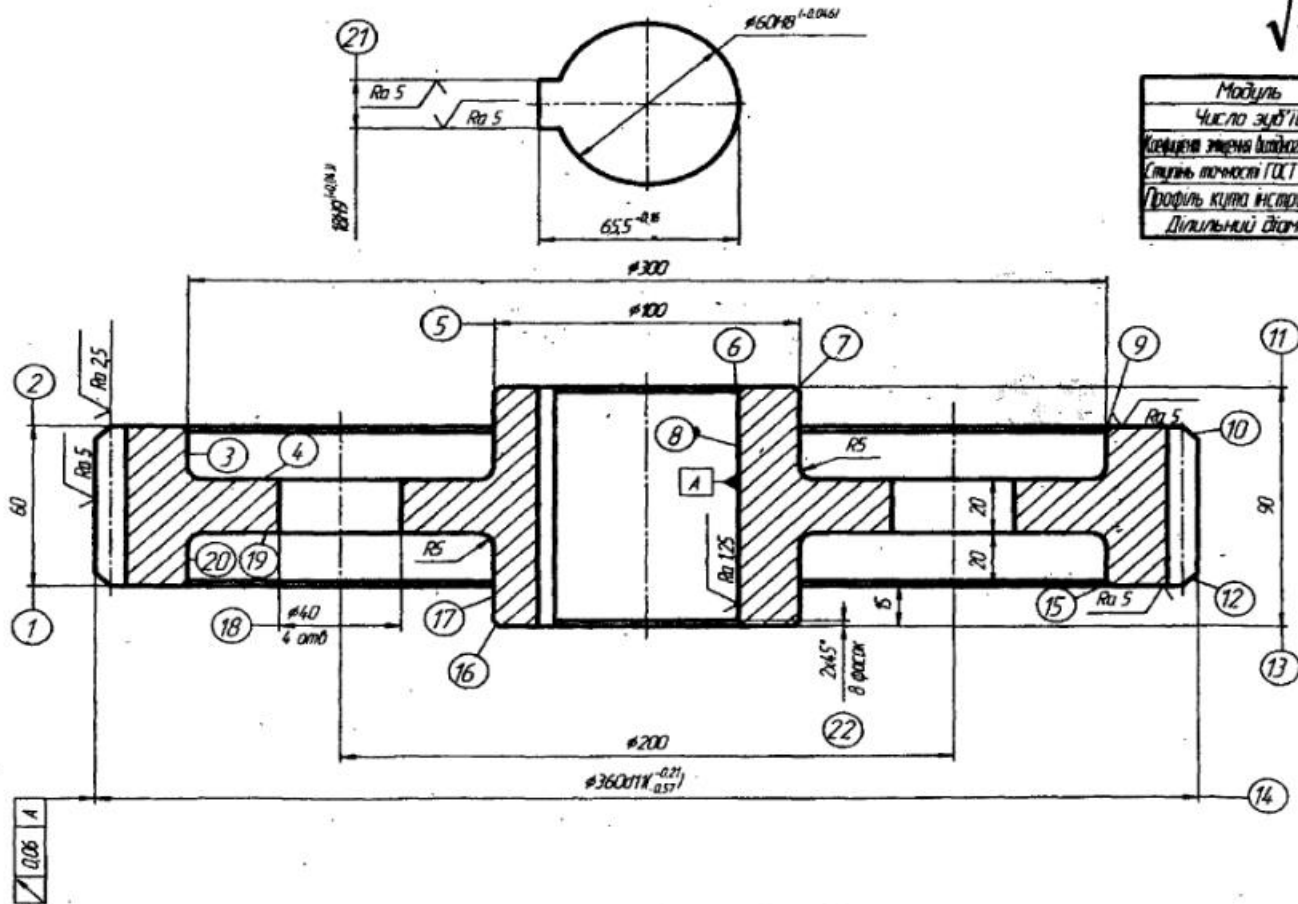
Эскиз детали «Зубчатое колесо»
